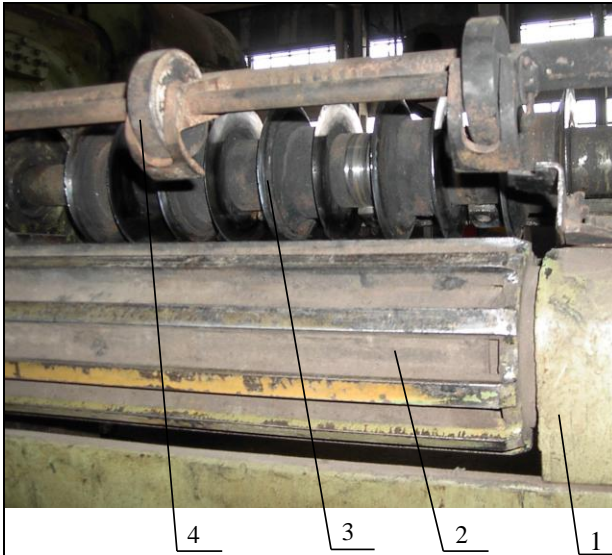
Конструкція зубчато-шліцевої передачі для подачі конвеєрної стрічки в зону різання:
